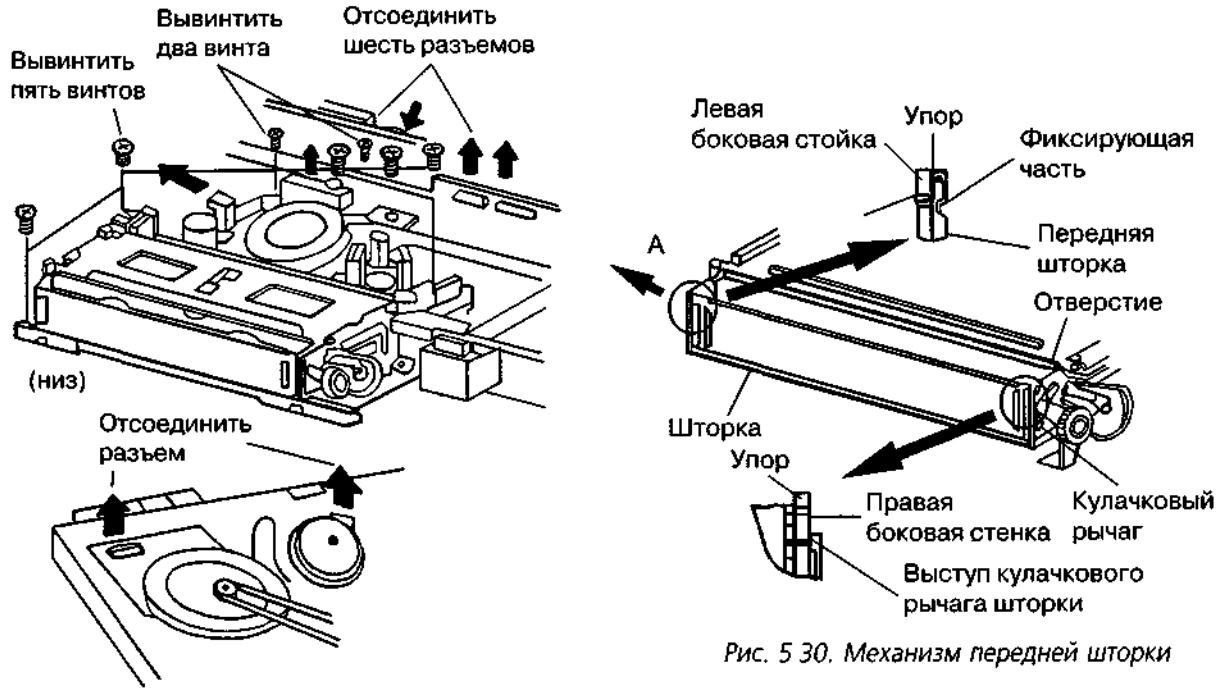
Схема извлечения блока лентопротяжного механизма из корпуса ВМ
